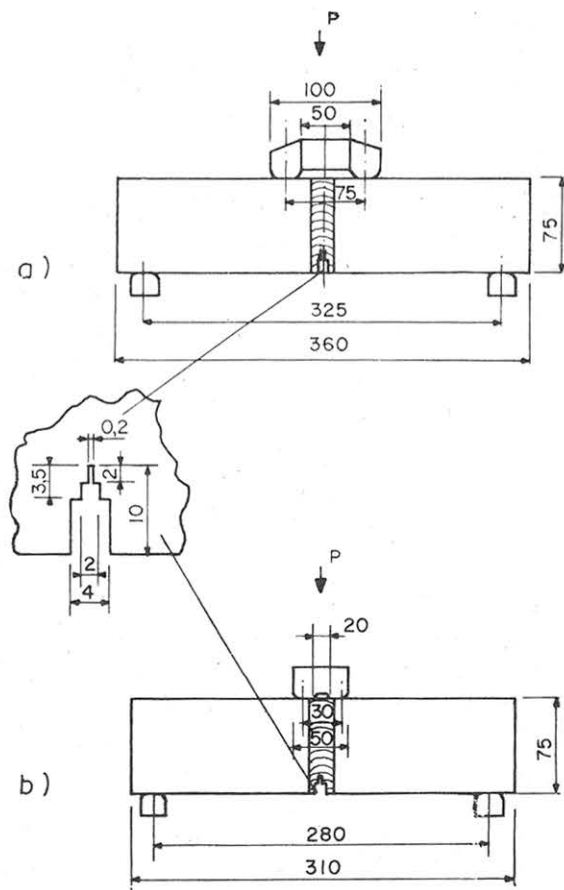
a) Probeta Niblink T de 360 mm. Espesor igual al de la chapa ensayada. Sobrecordón eliminado por mecanizado. b) Probeta Niblink T de 310 mm. Espesor igual al de la chapa ensayada. Sobrecordón eliminado por mecanizado.
